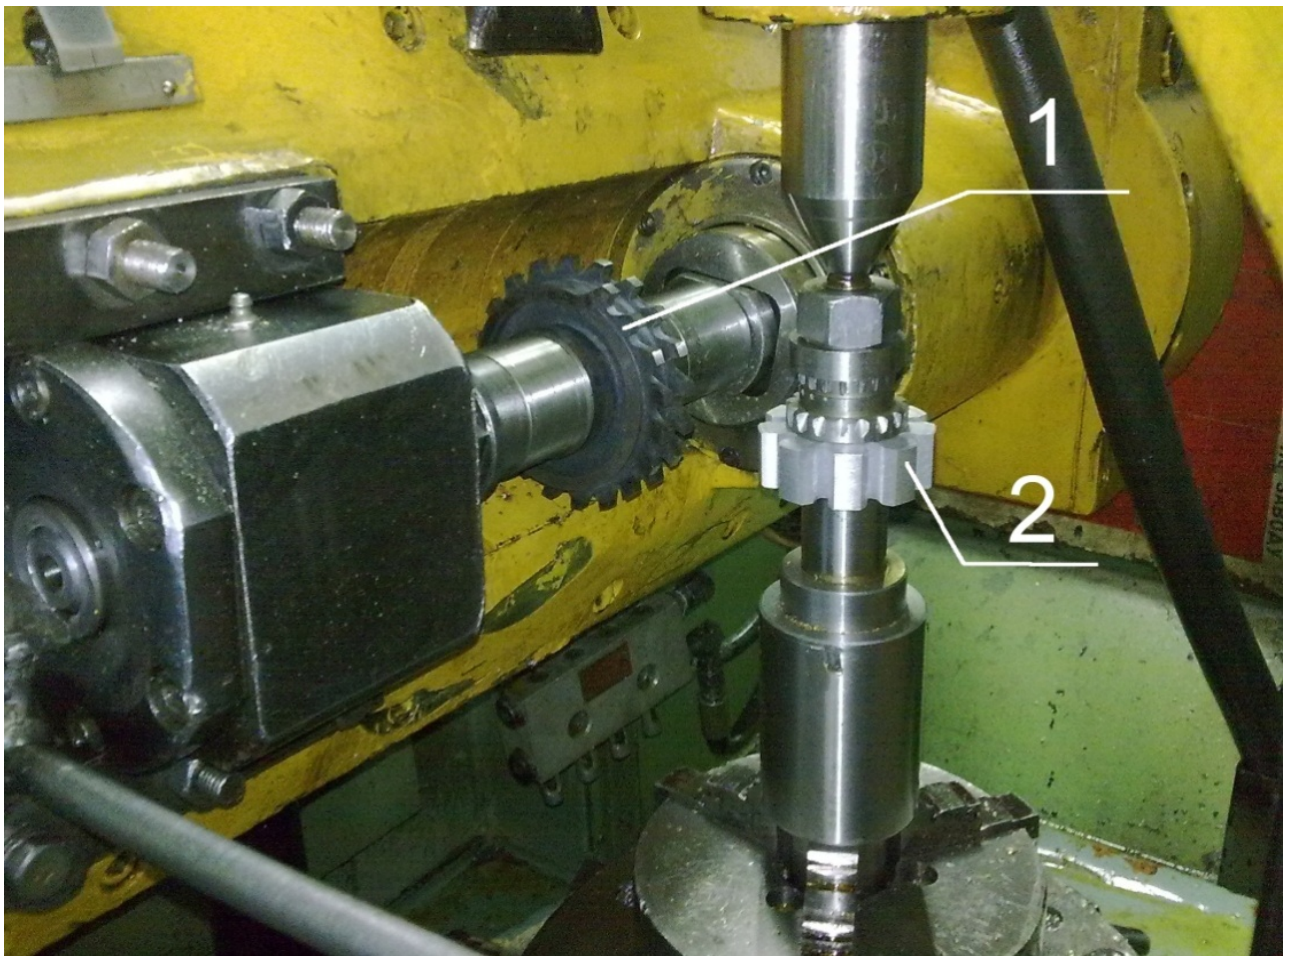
Робоча зона верстата 53А30П під час обробки
